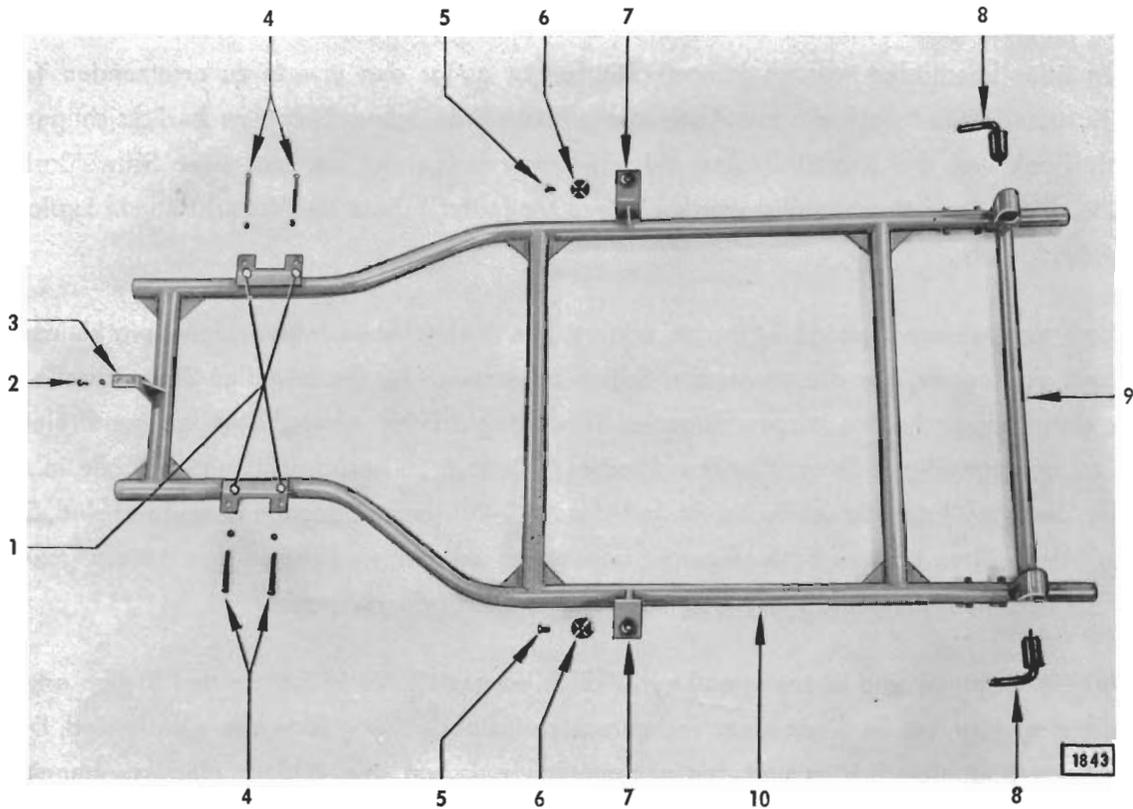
Vorderrahmen-Schweißblehre S-1195
